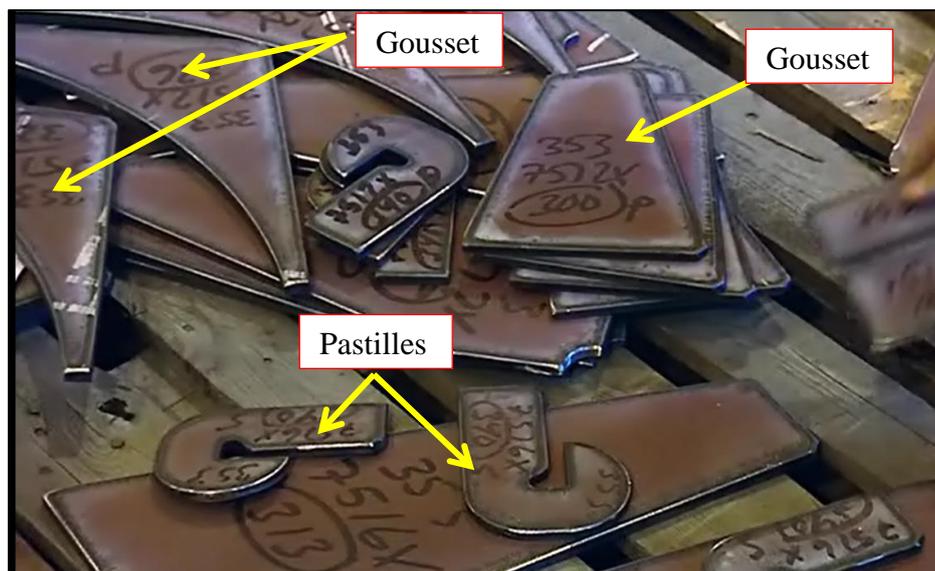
Pastilles de l'étanchéité et les goussets d'assemblages.
